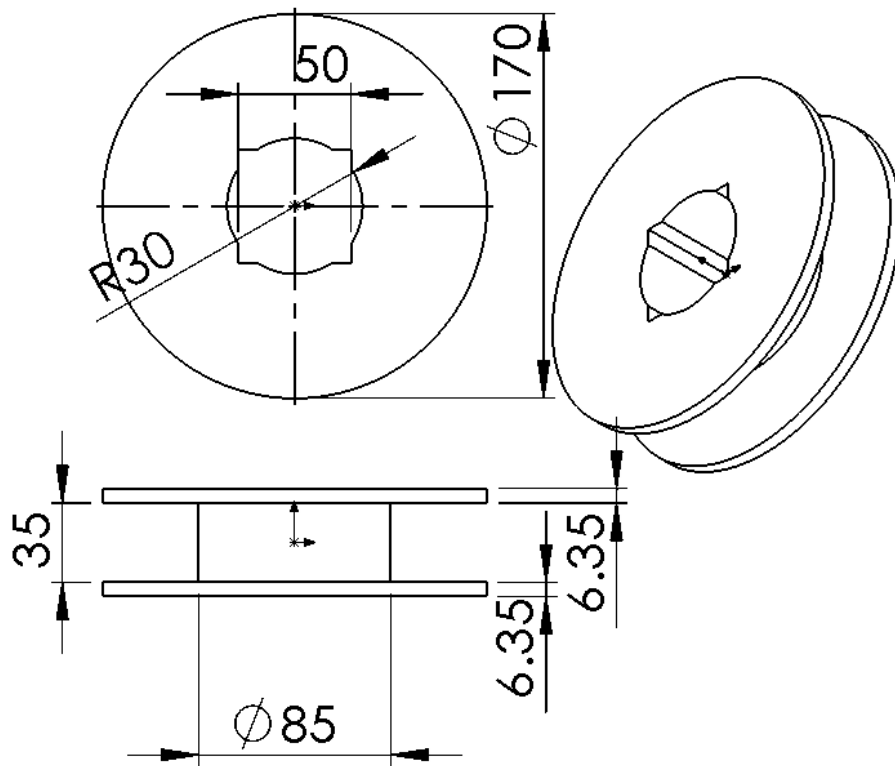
Dimensiones del carrete superior de las bobinas Helmholtz.
